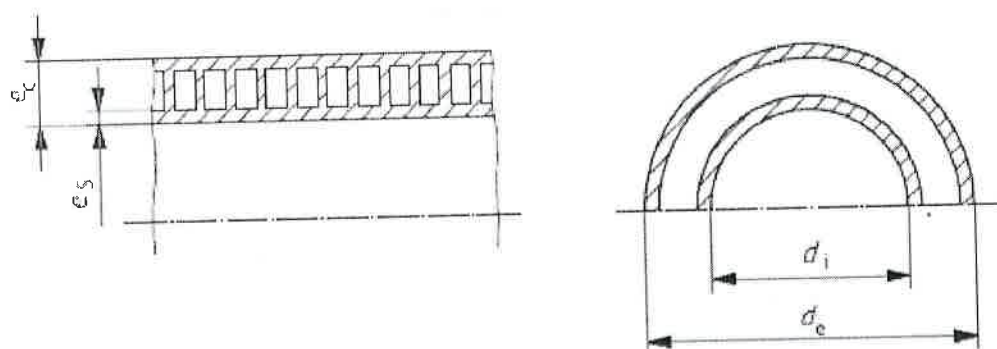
EJEMPLO TÍPICO DE CONSTRUCCIÓN DE PARED TIPO A2
